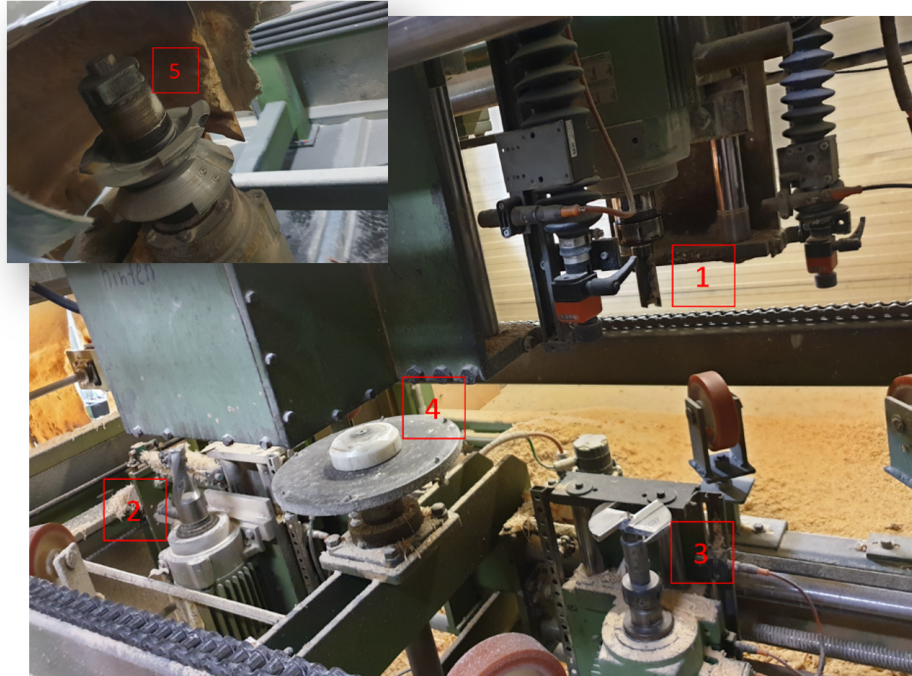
Übersicht der Werkzeuge in der E-Frässtation
